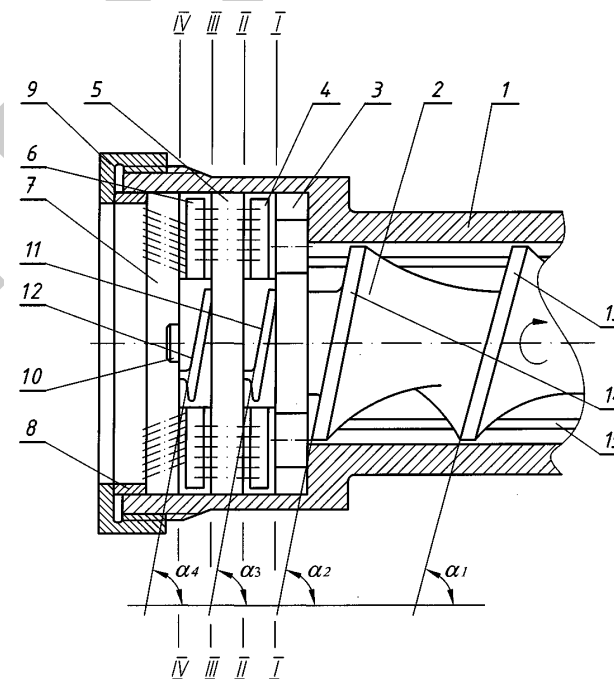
Схема режущего механизма волчка с наклонными ножами (продольный разрез): 1 – корпус; 2 – шнек; 3 – решетка подрезная; 4, 6 – ножи; 5, 7 – приемная и выходная решетки; 8 – кольцо; 9 – гайка; 10 – вал; 11, 12 – передние наклонные грани ножей 4 и 6; 13, 14 – наклонные ребра шнека 2; 15 – продольные ребра; I, II, III, IV – плоскости резания; $\alpha_1, \alpha_2, \alpha_3, \alpha_4$ – углы наклона витков шнека и наружных граней ножей 4 и 6
